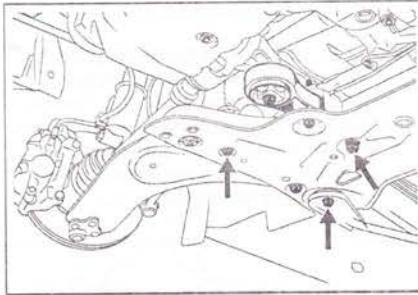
Опустите подрамник в сборе с рычагами подвески и стабилизатором поперечной устойчивости, повернув штангу стабилизатора, чтобы избежать ее зацепления за рулевой механизм.
